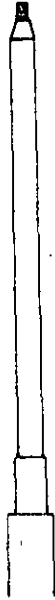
Presure el cable de acero con el extracto incluido en cada estuche.
